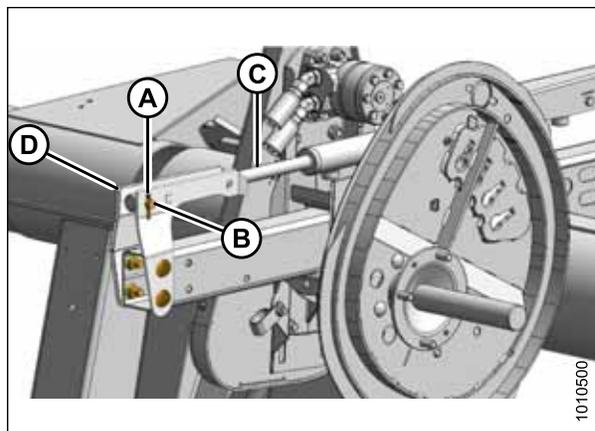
Центральный рычаг мотовила в переднем положении
